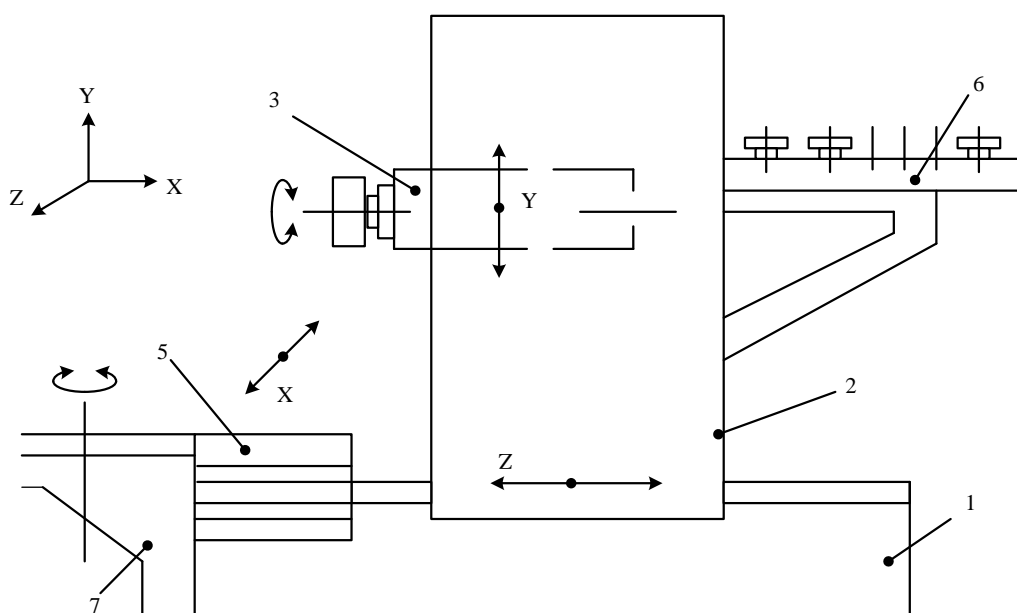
Багатоопераційний верстат з ЧПК мод. BEA2 фірми Heller (Німеччина)
